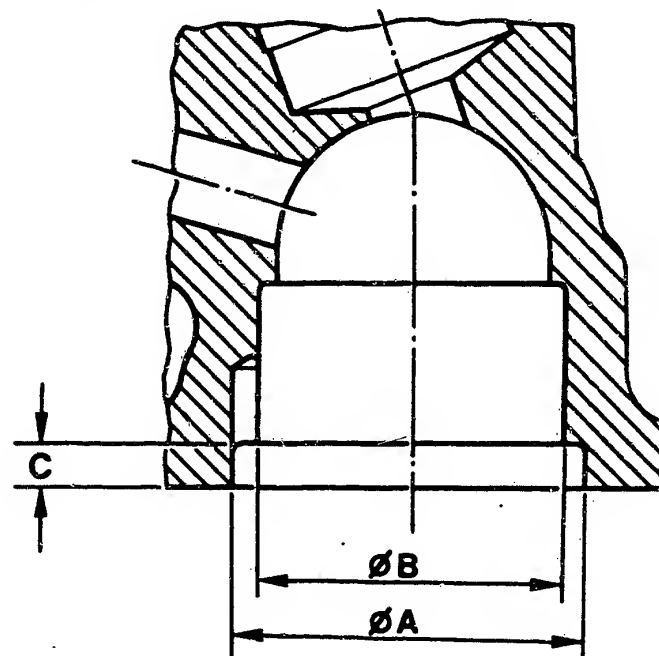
Diesel-Motor: Wirbelkammer im Schnitt: A und B siehe Tabelle.
